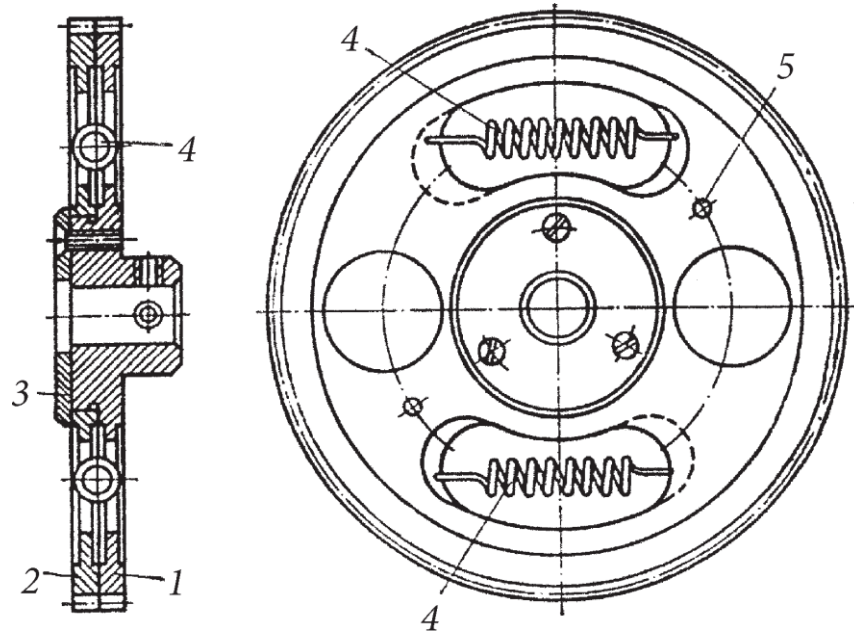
Автономный механизм для выборки люфта в зубчатой передаче
